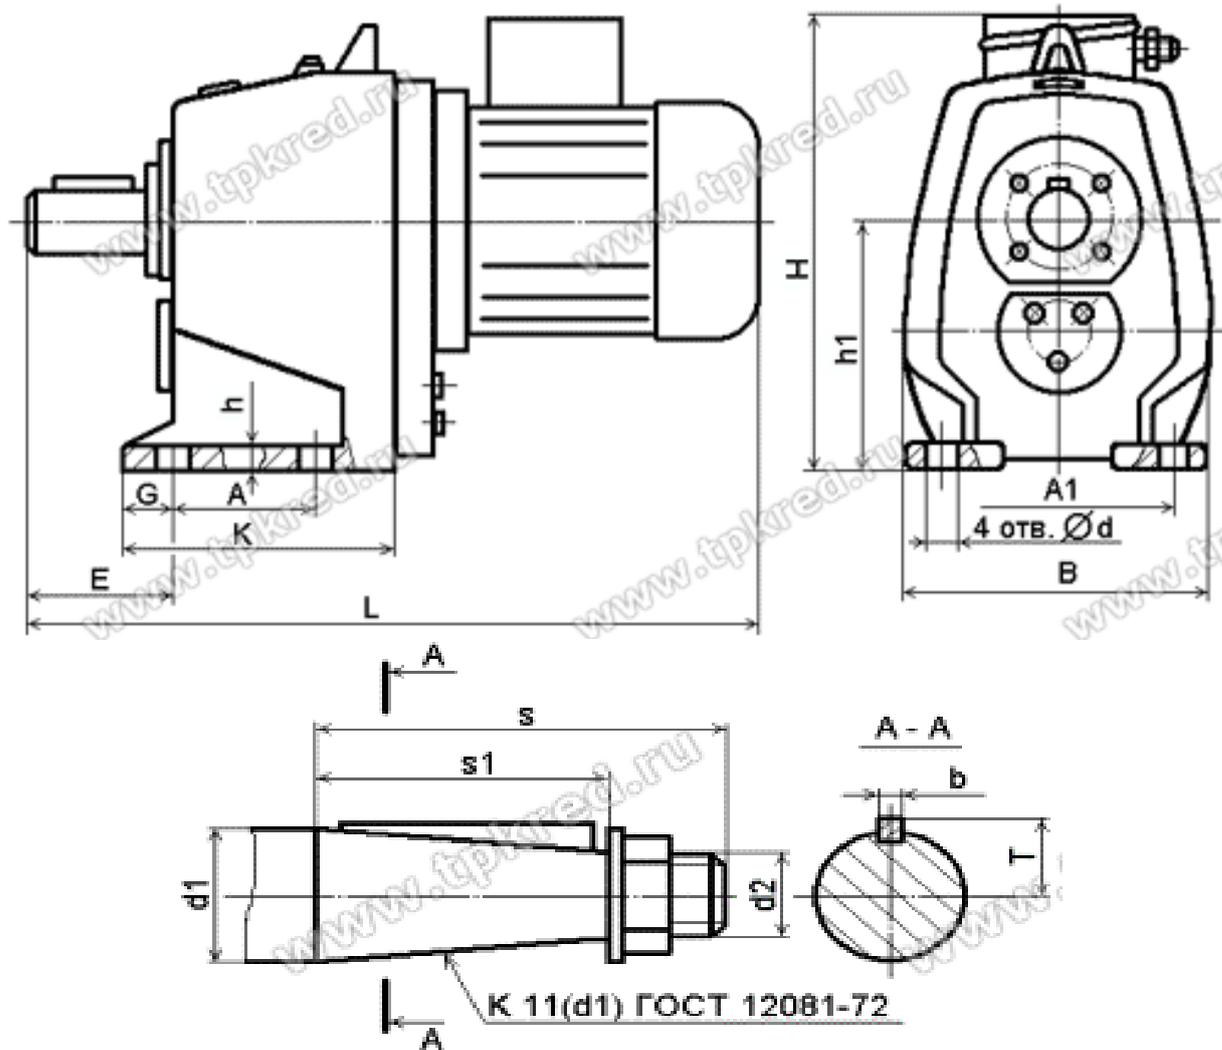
Габаритные размеры мотор-редуктора
